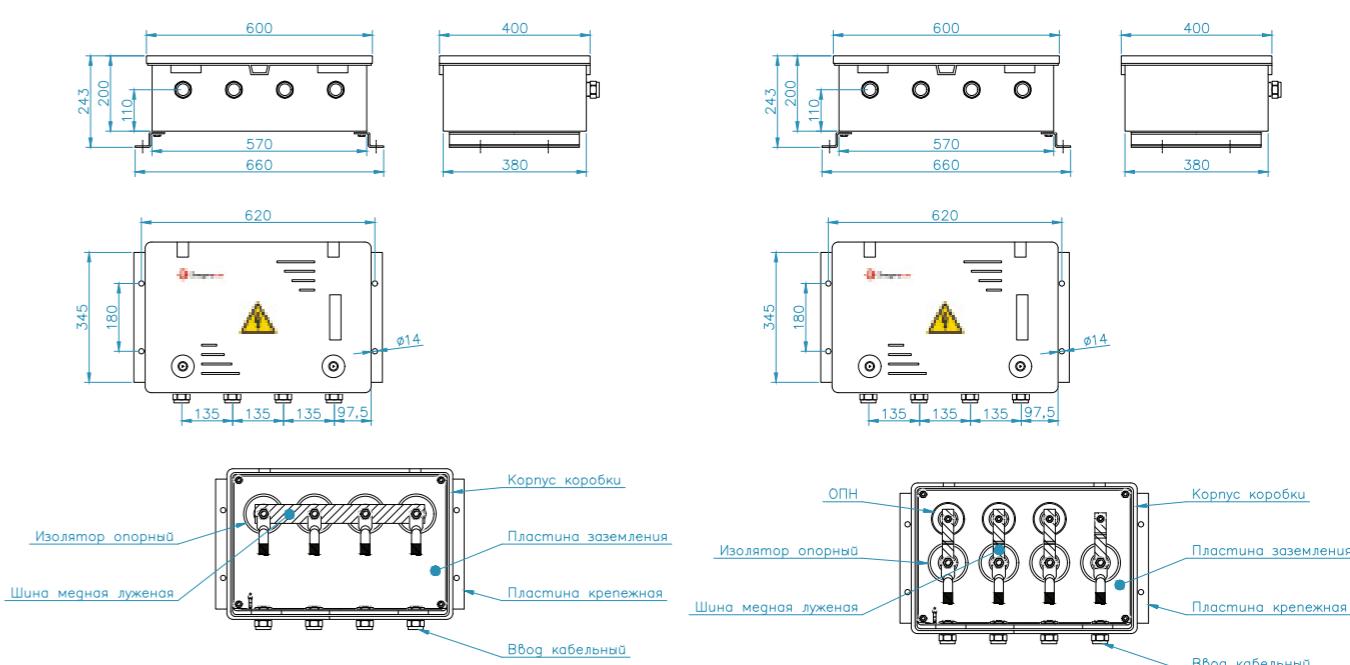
Чертеж коробки заземления ЭнергоТЭК КЗП-Т
